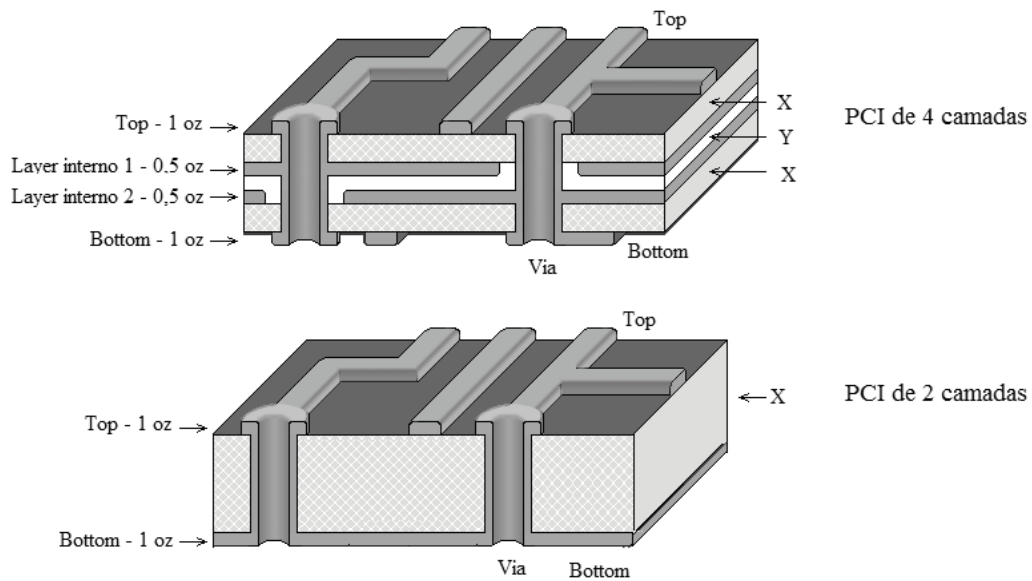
Detalhes sobre PCI de 4 e 2 camada.
